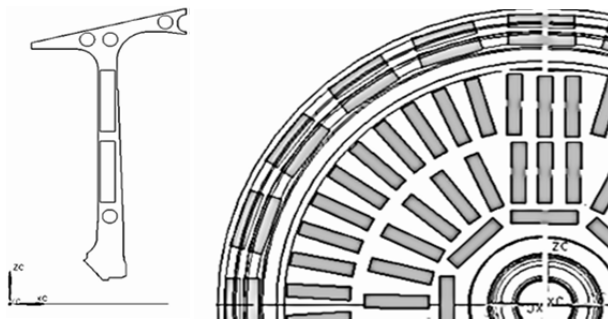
Схема разрезки диска 1-й ступени КНД на заготовки образцов
